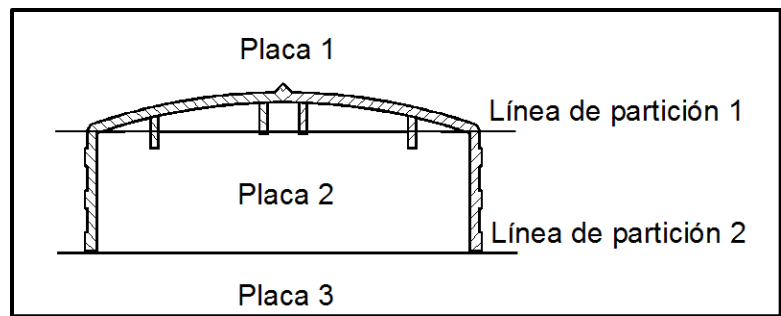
Placas propuestas para el diseño del molde de inyección
